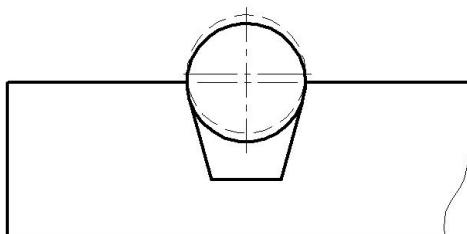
Похибка положення заготовки в захватному пристрої
